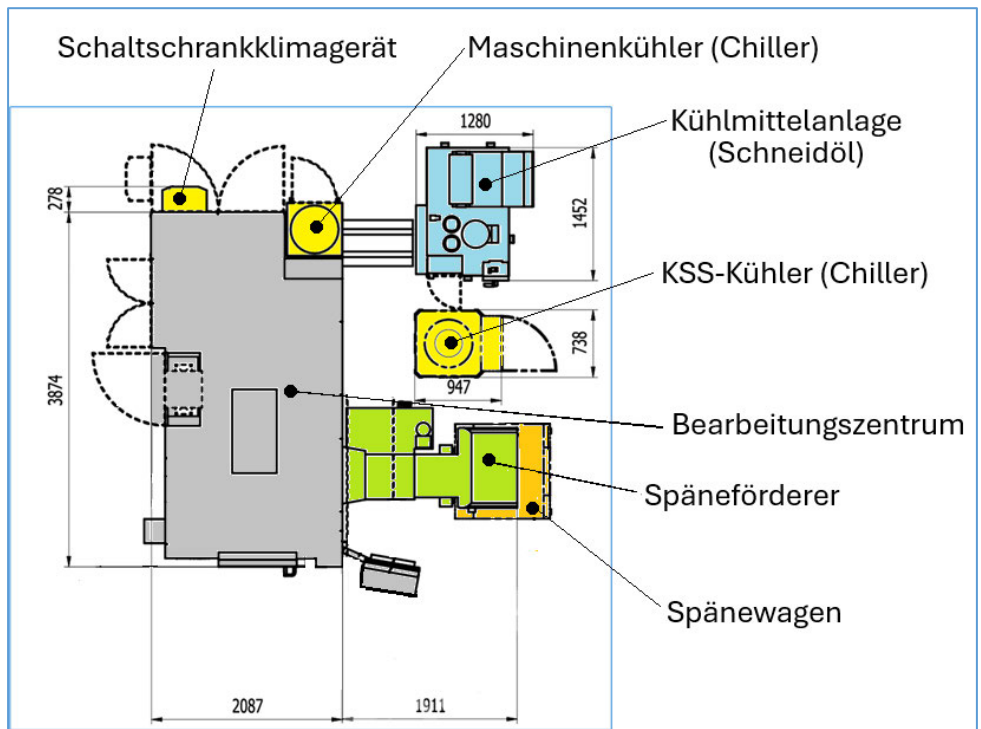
Aufstellplan einer CNC-Werkzeugmaschine mit einem Schaltschrankklimagerät und zwei Chillern.
